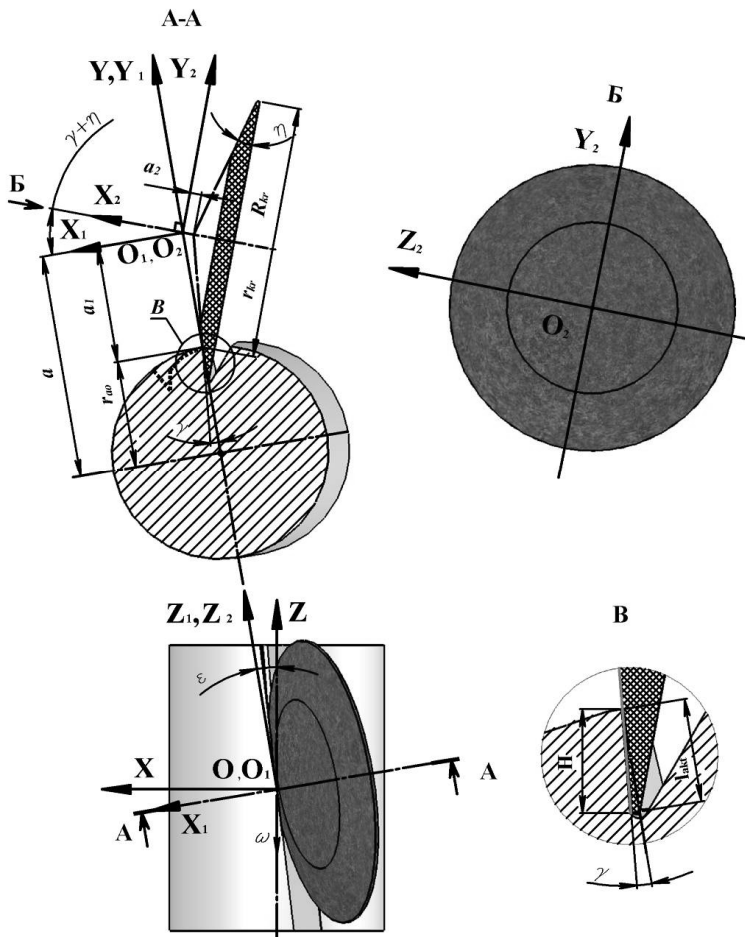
Установка заточного круга при утворенні передньої поверхні зуба фрези
